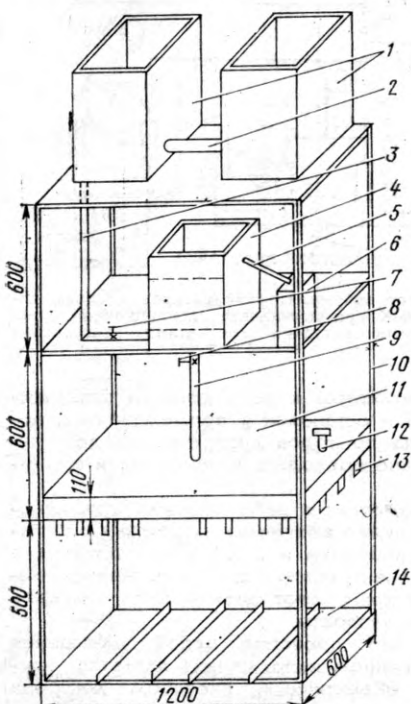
Дозатор для заливки электролита: 1, 4 — баки; 2, 3, 9 — соединительные трубы; 5 — дренажная труба; 6 — сливной бак; 7, 8 — краны; 10 — рама; 11 — коллектор; 12 — сапун; 13 — выводы коллектора; 14 — подставка
